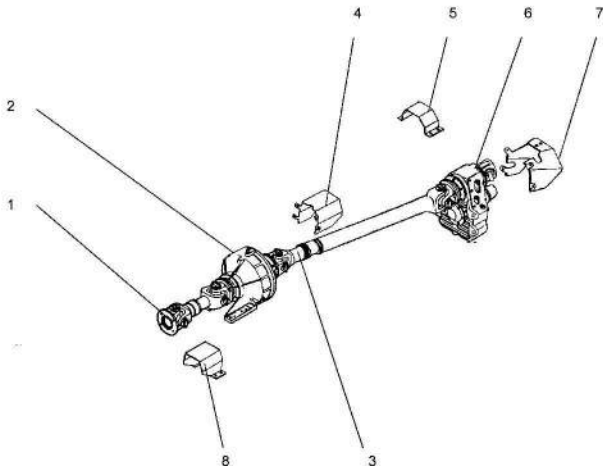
Карданная передача механизма отбора мощности: 1- карданный вал ведущий; 2- соединительная муфта; 3- карданный вал ведомый; 4,5,7,8- кожух; 6- редуктор.
